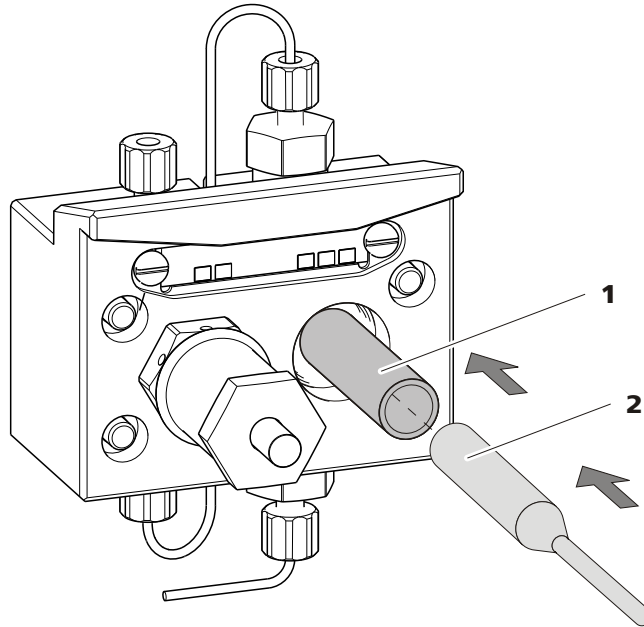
Kolbendichtung in Pumpenkopf einsetzen
